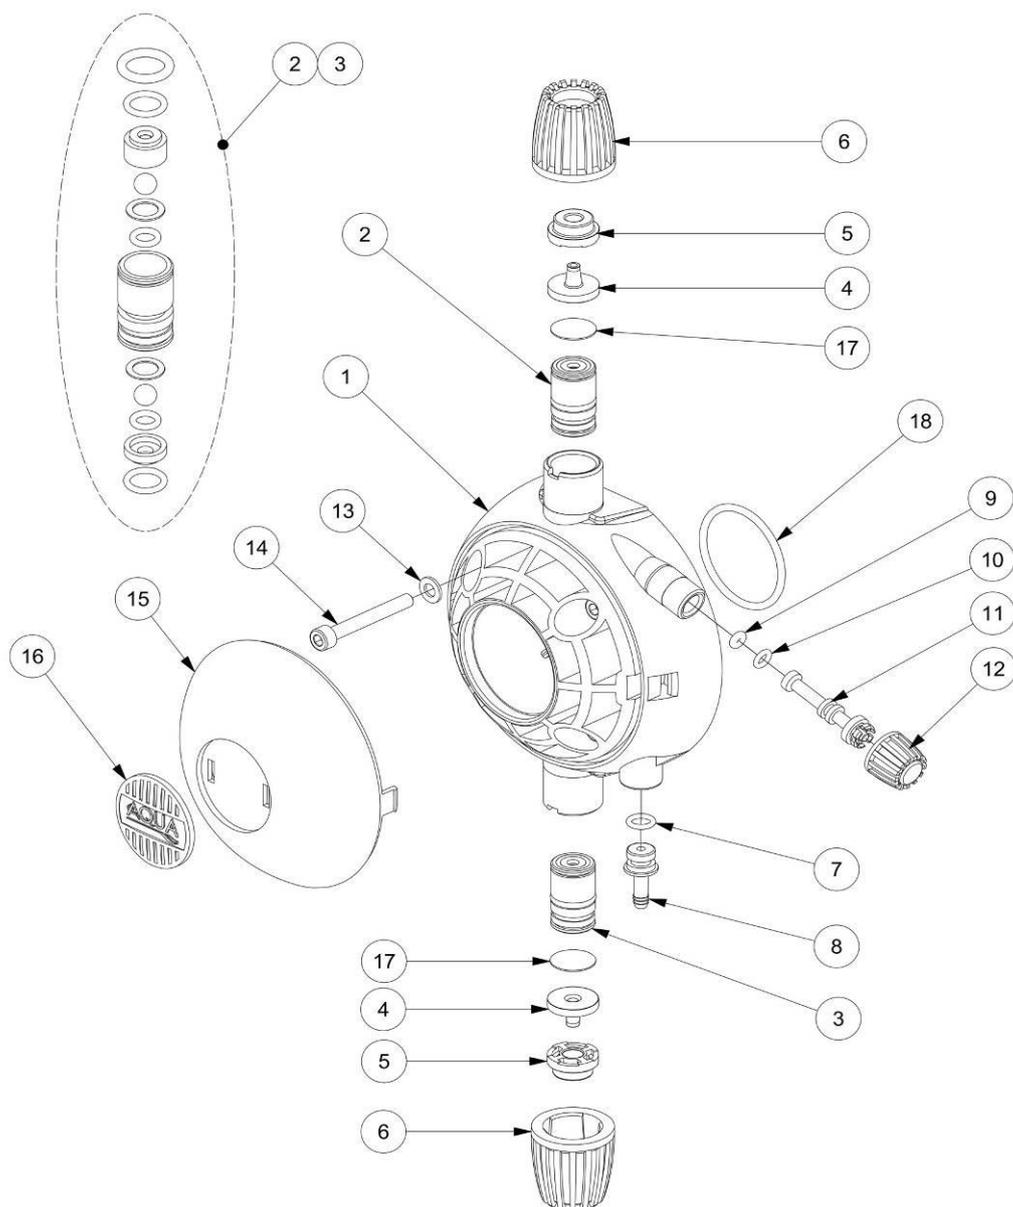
SERIE HC 999 - Esploso / Description / Explose / Dibujo / Explosionszeichnung / Чертеж
